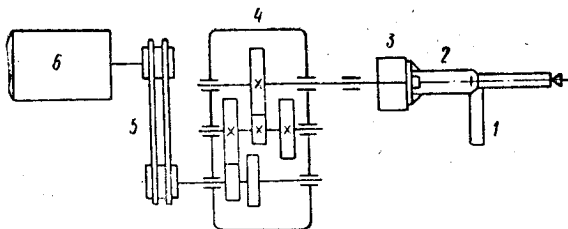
Типовая кинематическая схема коробки скоростей токарного станка с двухскоростным электродвигателем:
